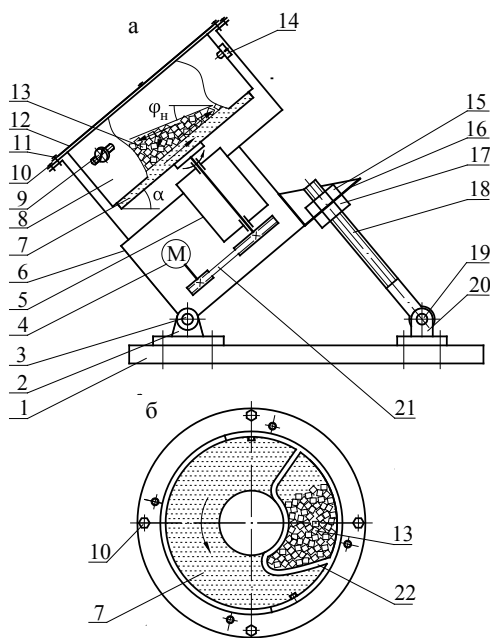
Установка для предварительного шлифования шариков из кубиков: а – схема установки; б – рабочая зона
